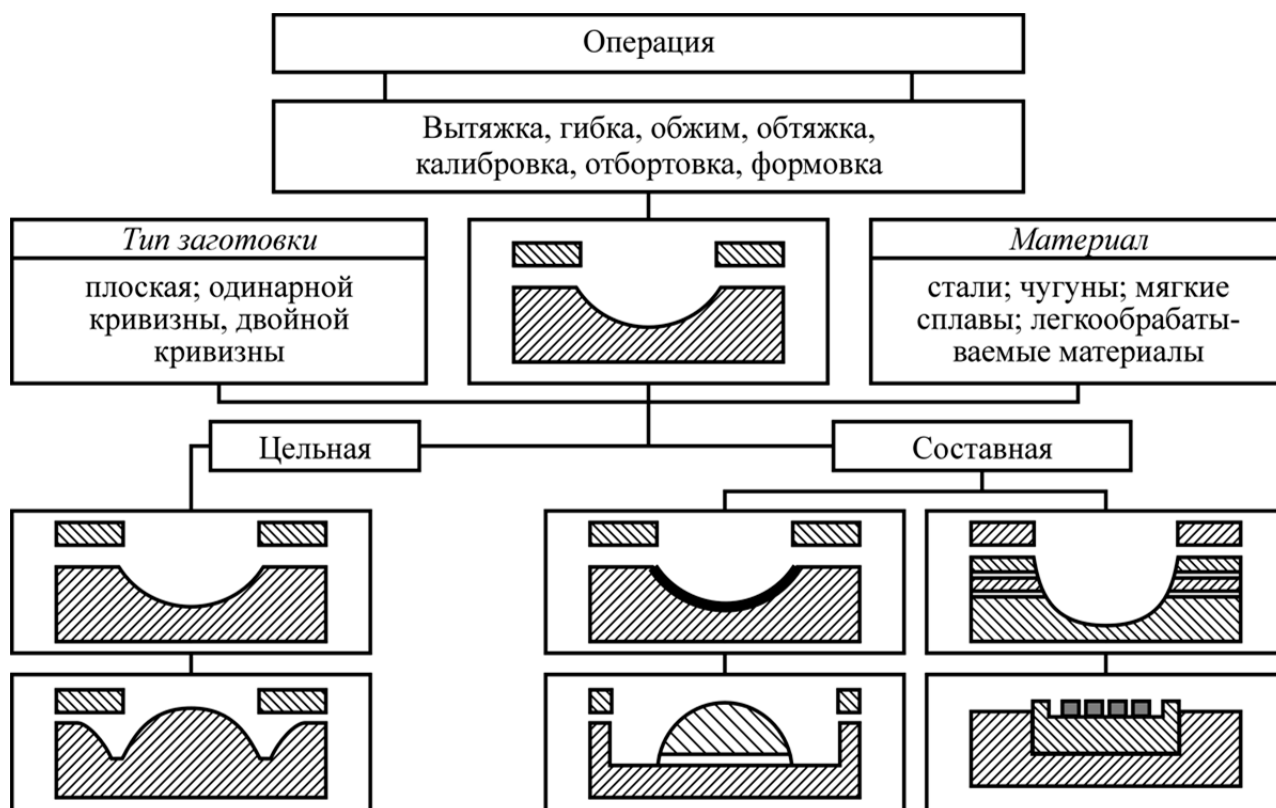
Конструктивные схемы штампов для изготовления деталей из плоских заготовок
